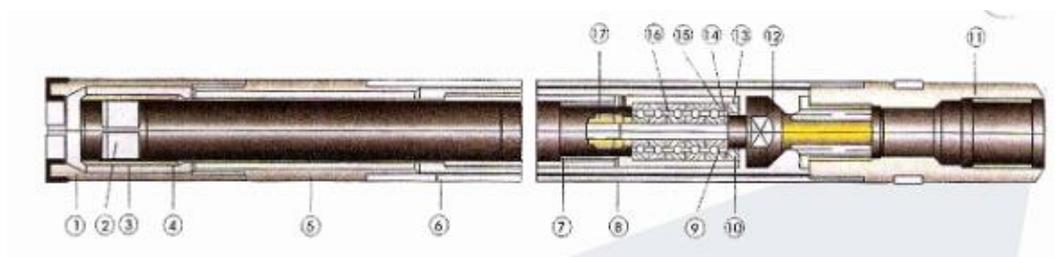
Конструкция двойной колонковой трубы Т2-76 «TECSO S.A.»:
